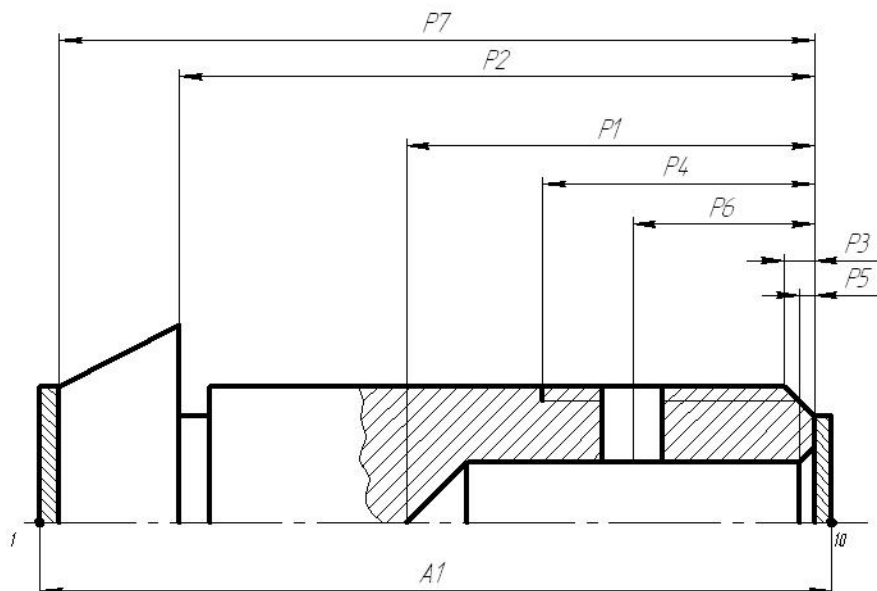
Эскиз детали с условными обозначениями размеров
